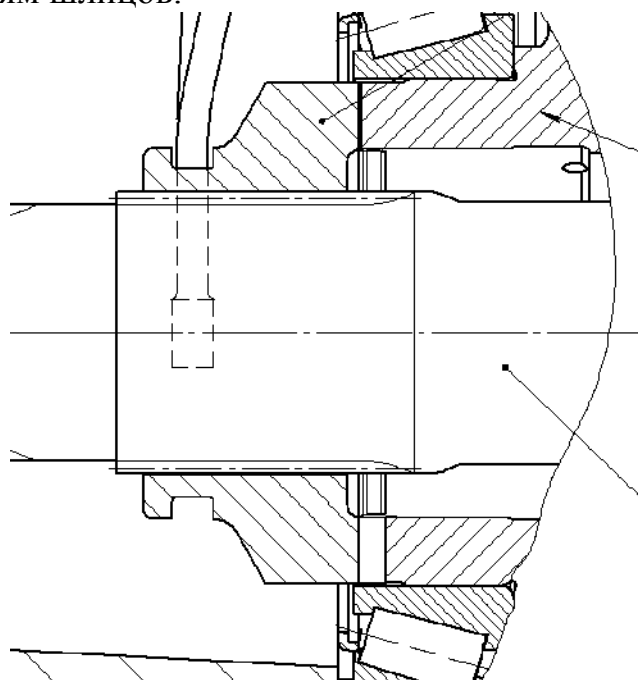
Общий вид шлицевого соединения муфты блокировки межосевого дифференциала и вала солнечной шестерни дифференциала
